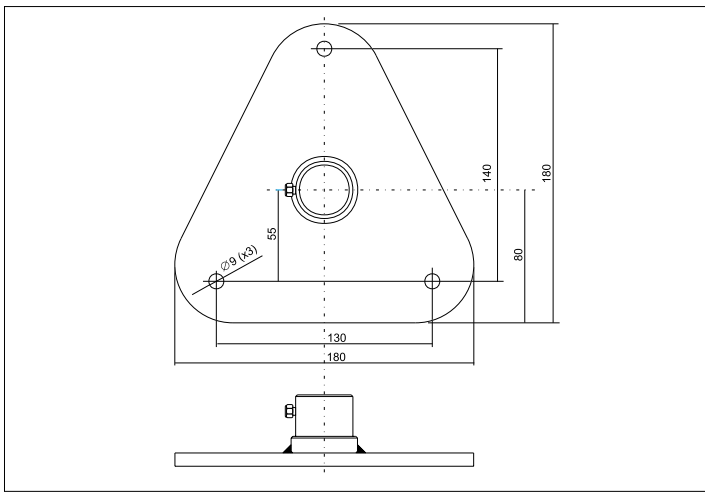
Base per fissaggio a pavimento (HD2013.78)
